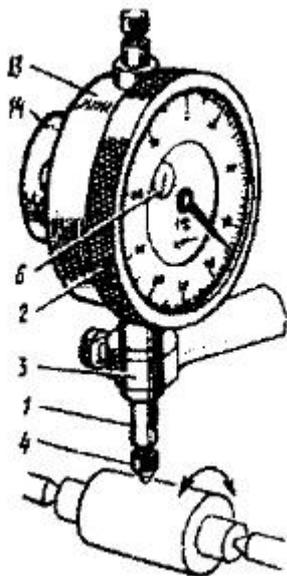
Установка для проверки отклонения цилиндрических поверхностей.
